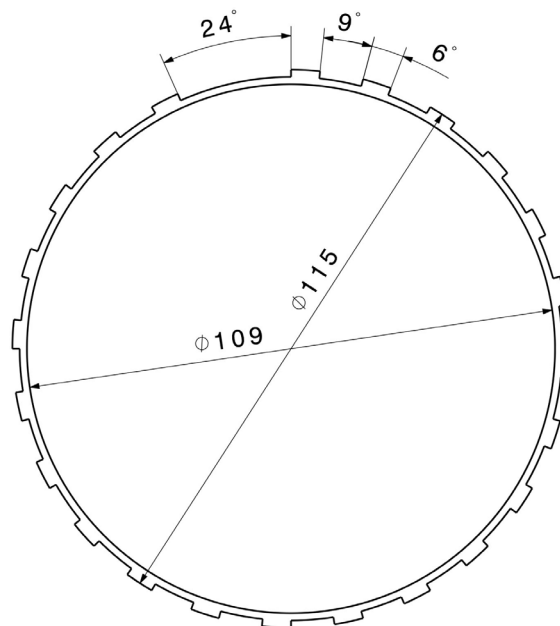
Triggerring für das Motorsteuergerät M3A
